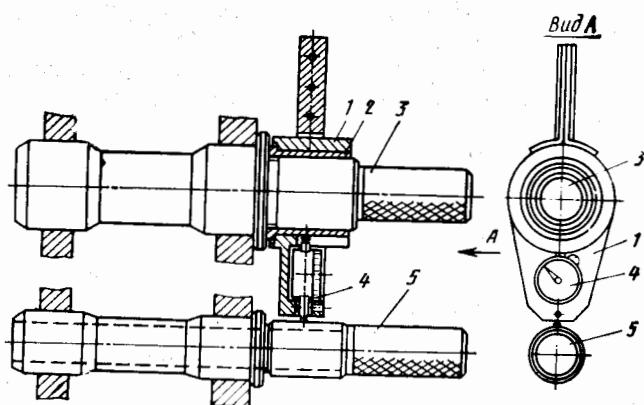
Приспособление для измерения межцентрового расстояния отверстий коренных подшипников блока цилиндров и втулок распределительного вала
